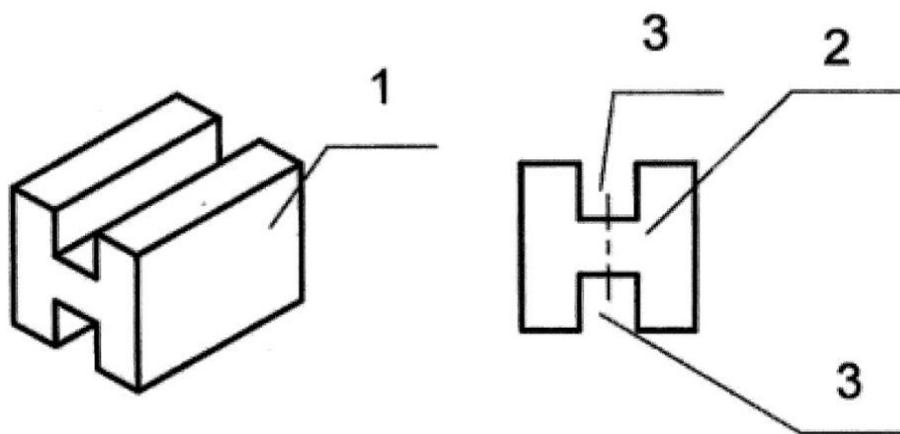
Конструктивная схема зубочелюстного тренажера (1 – общий вид устройства, 2 – Н-образная форма, 3 – прорези).
